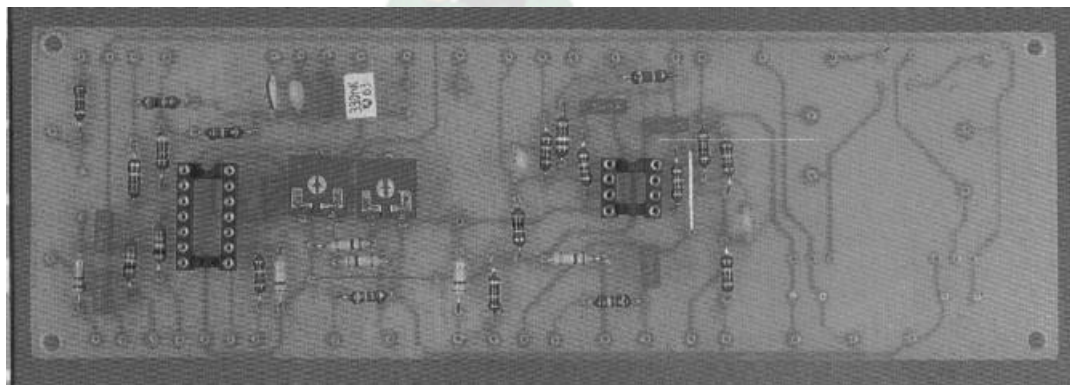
Soldadura de los componentes no polarizados de menor altura
